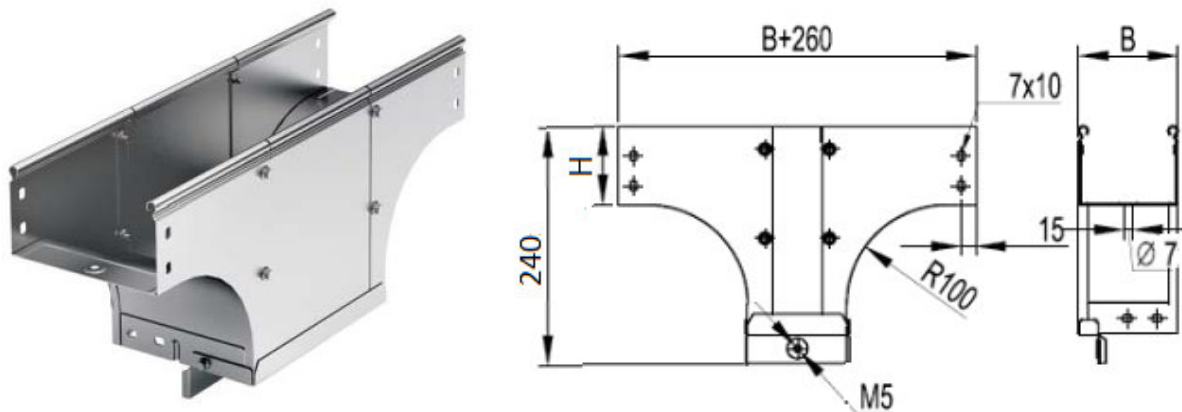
Ответвитель TDS T-образный вертикальный универсальный, типов: 3758, 3716, 3717
